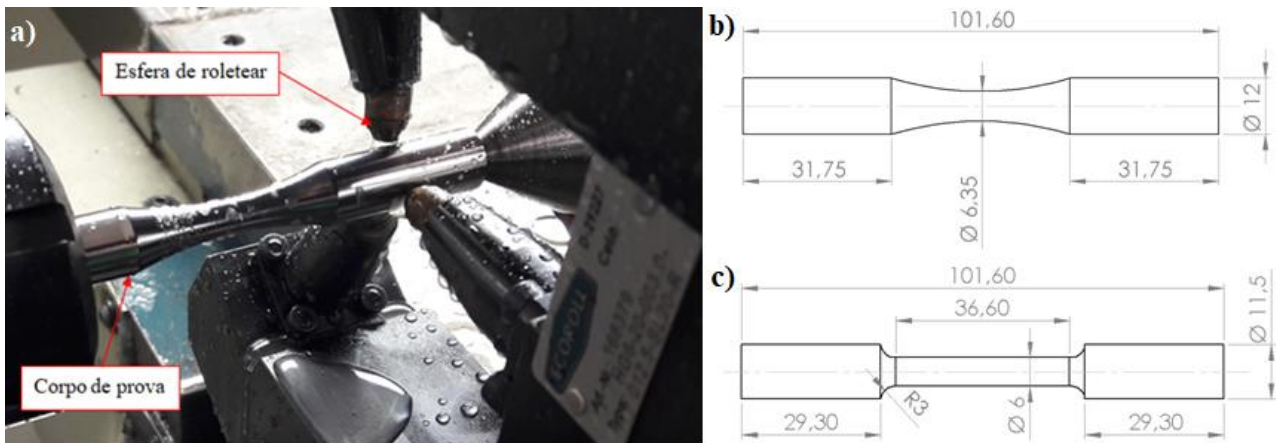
a) Ferramenta de roletear acoplada ao torno e dimensões (em mm) do corpo de prova b) fadiga e c) tração.
